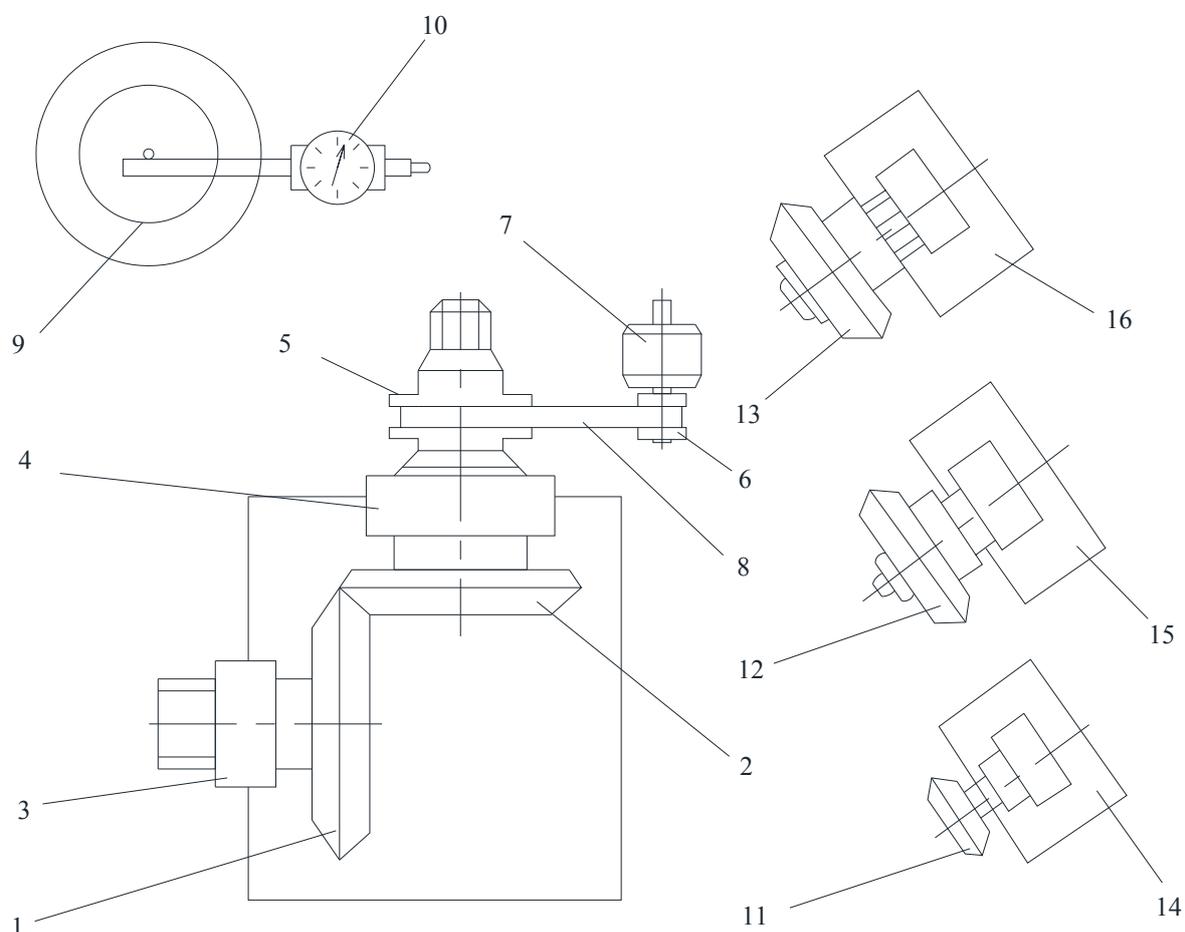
Схема стенда для измерения сборки конических зубчатых передач: 1–2 – вал шестерни; 3,4 – втулки; 5,6 – шкивы; 7 – электродвигатель; 8 – плоский ремень; 9 – штатив; 10 – индикатор; 11, 12, 13 – зубчатые колеса; 14, 15, 16 – стойки со втулками
